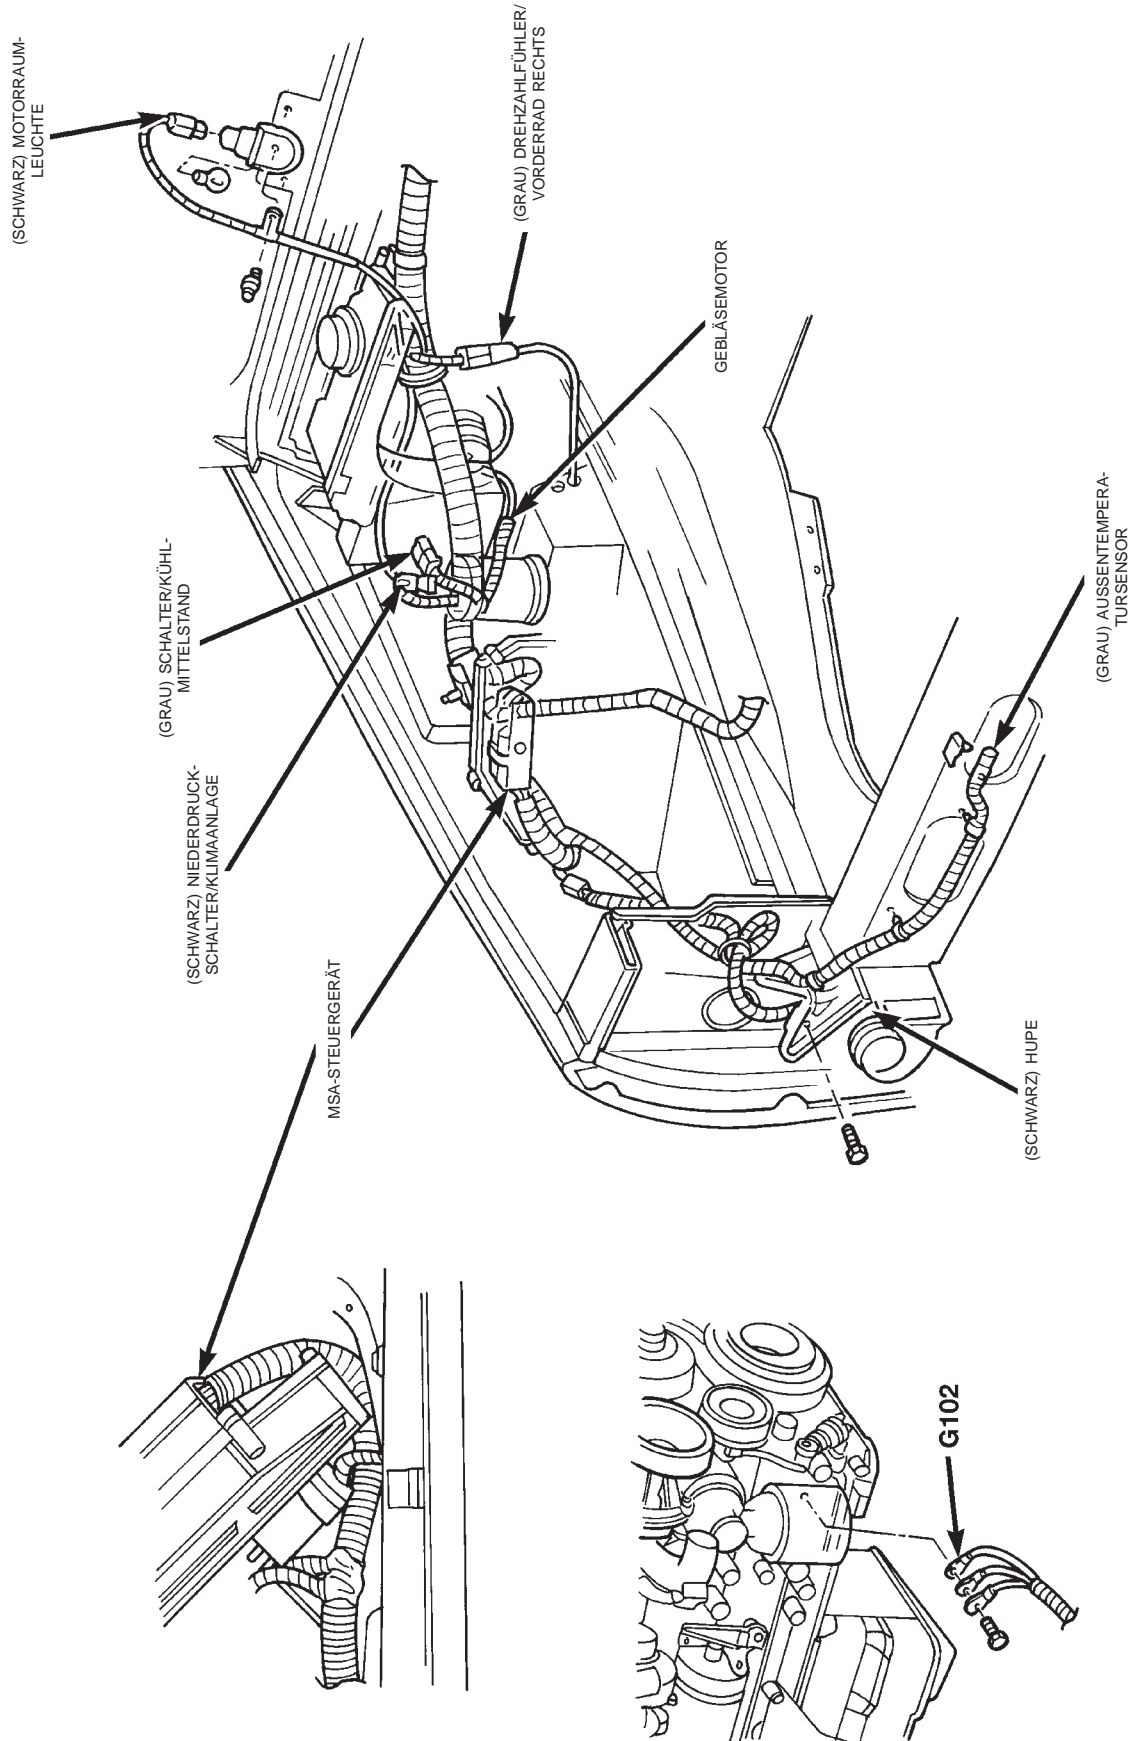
Motorraum rechts Dieselmotor Linkslenker
